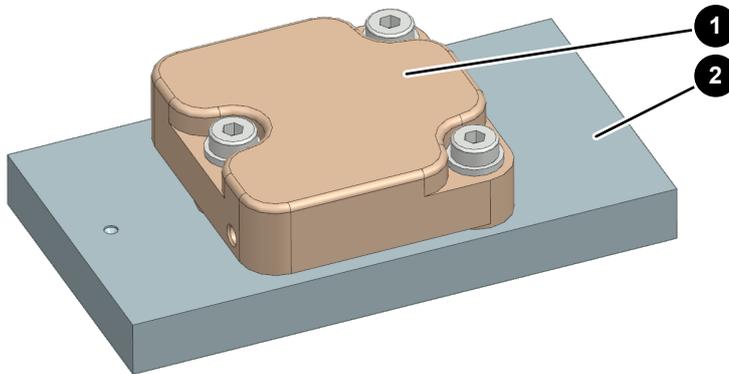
Montage des Pulsotronic-Sensors auf der GFK-Montageplatte
